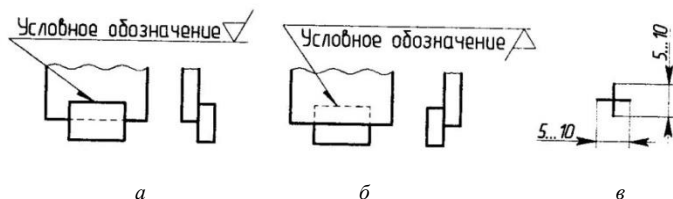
Сварные швы и точки на чертеже:
